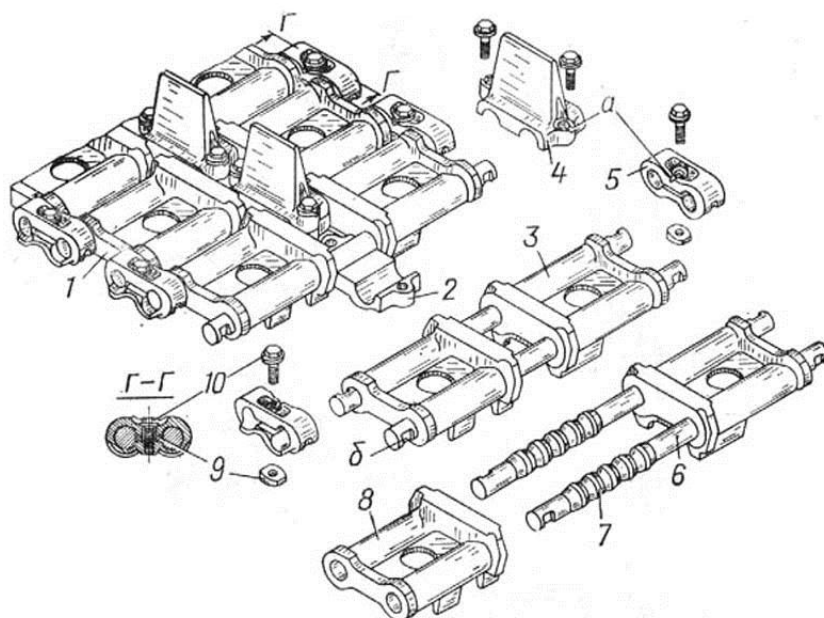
Гусеница: 1 - гусеница; 2 - ба́шмак; 3 - трак; 4 - гребень; 5 - соединительная скоба; 6 - пальцы; 7 - резиновое кольцо; 8 - звено трака (плица); 9 - клин; 10 - болт; 11 - шайба
